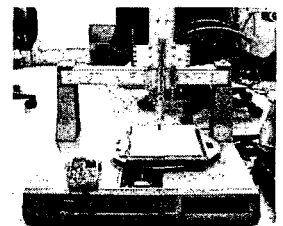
은 본 논문의 타당성의 입증하기 위해 제작 한 PCB 및 적용한 기구부이다.
